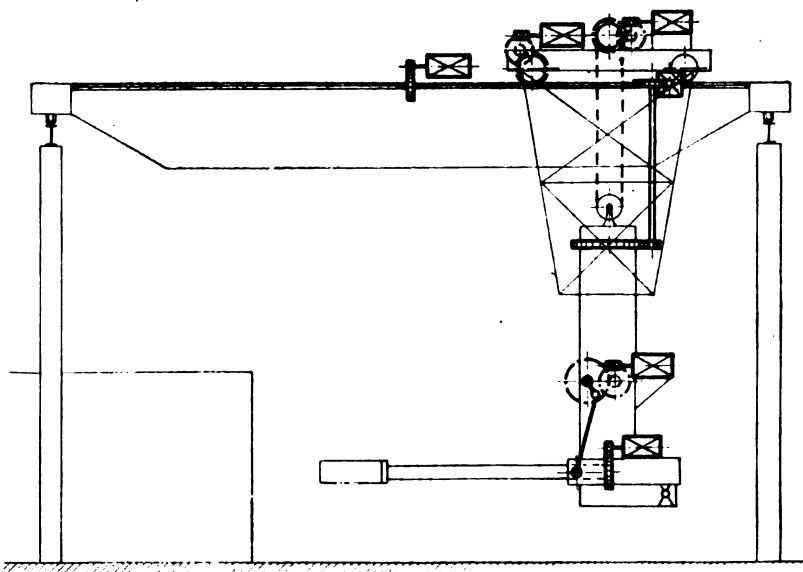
Beschickkran mit ringsum drehbarem Schwengel sowie gleichzeitiger Wipp- und senkrechter Hubbewegung.
